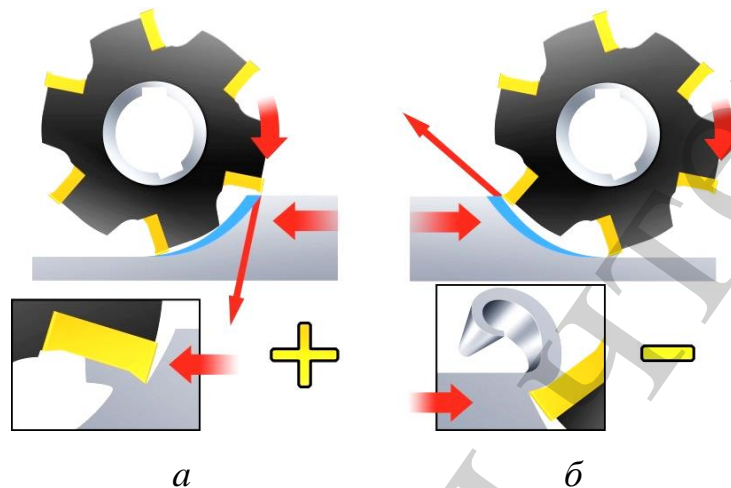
Способи фрезерування, обумовлені напрямком руху заготовки щодо інструмента; а – попутне фрезерування; б – зустрічне фрезерування
